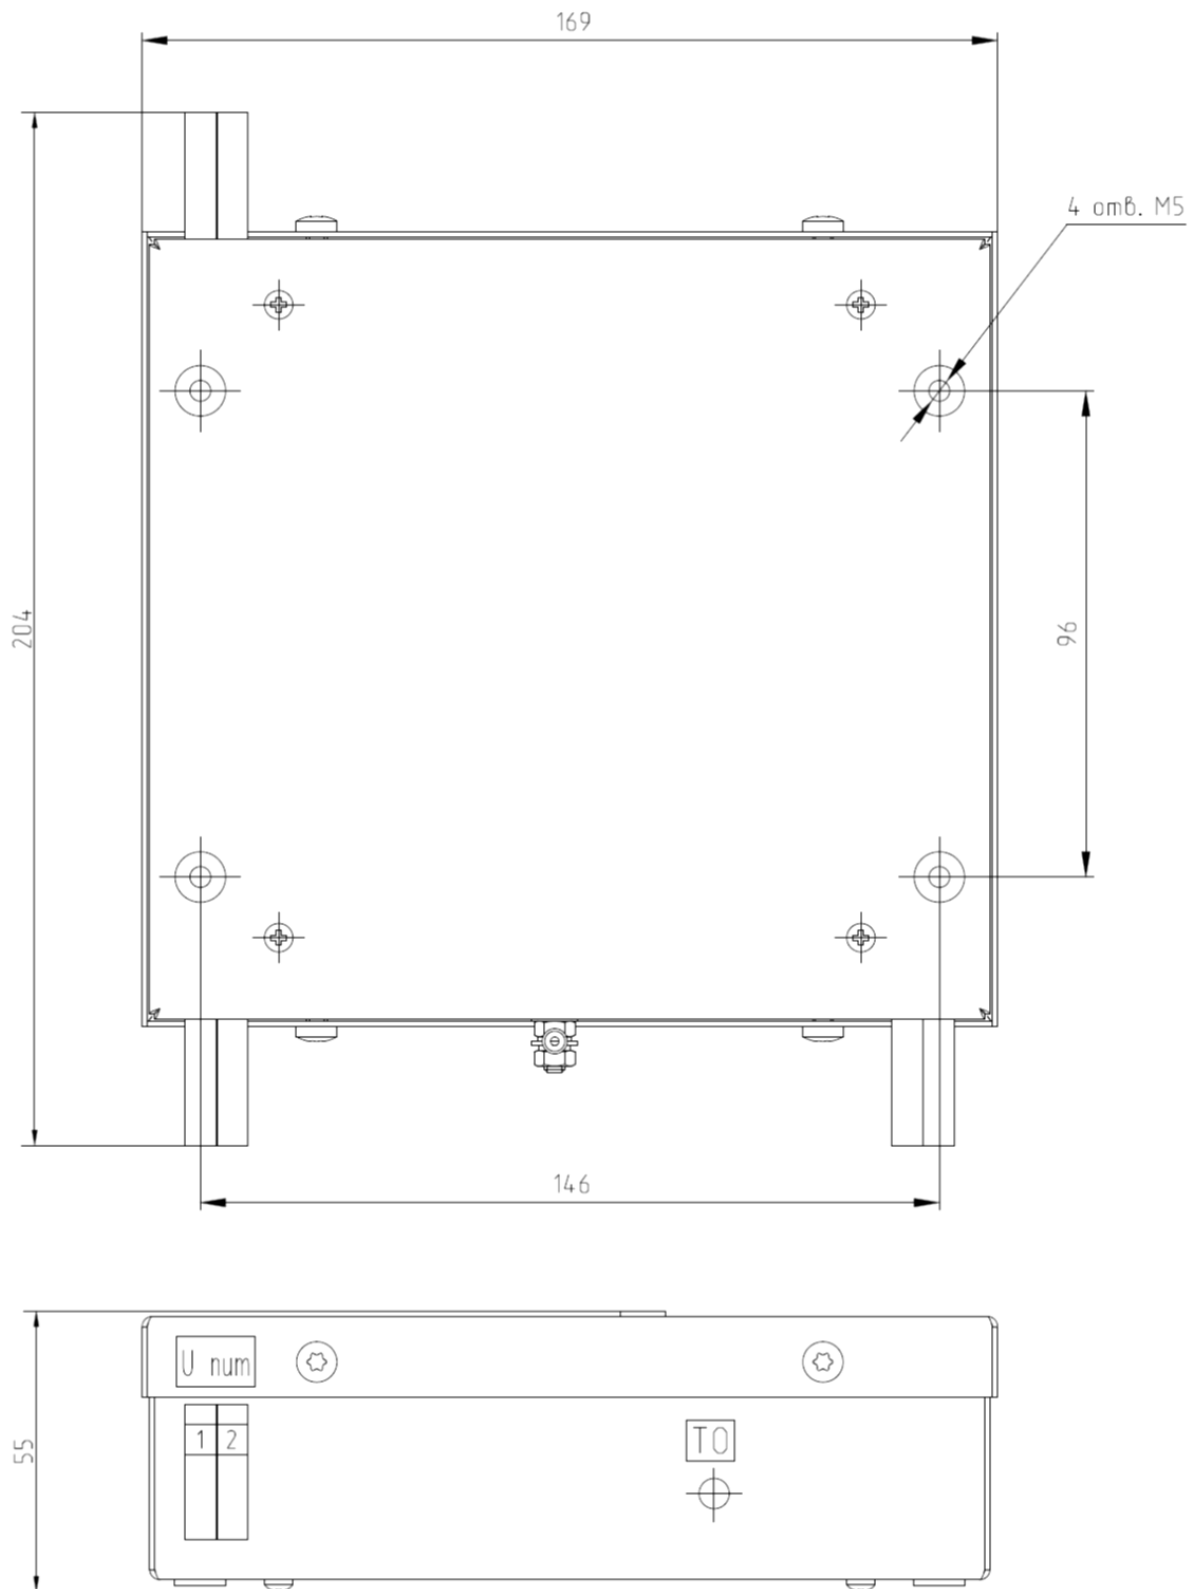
Габаритные и установочные размеры блока БР-1000
